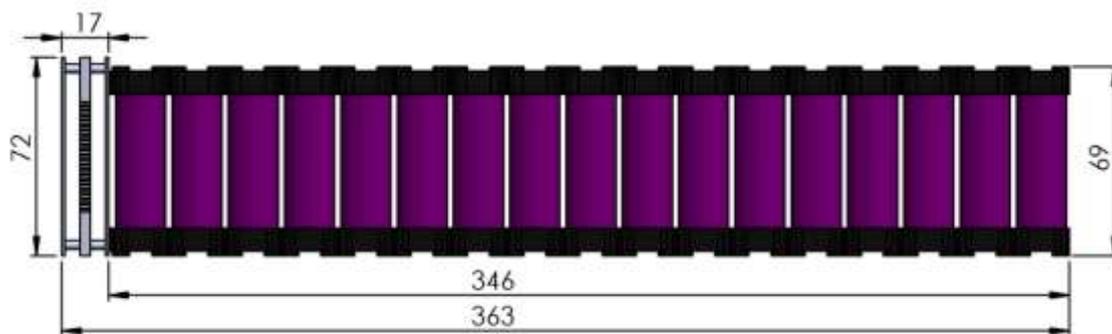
Vista lateral, banco de batería de 60V 30Ah (17S 12P)
